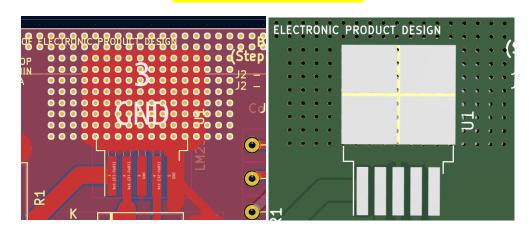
ผลการแบบ PCB (Bottom Layer)
